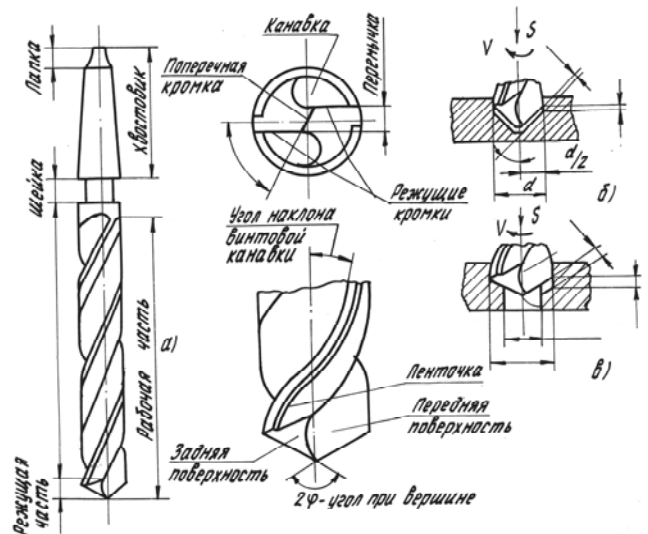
Элементы сверла и схемы сверления: а) элементы сверла, б) сверление; в) рассверливание
